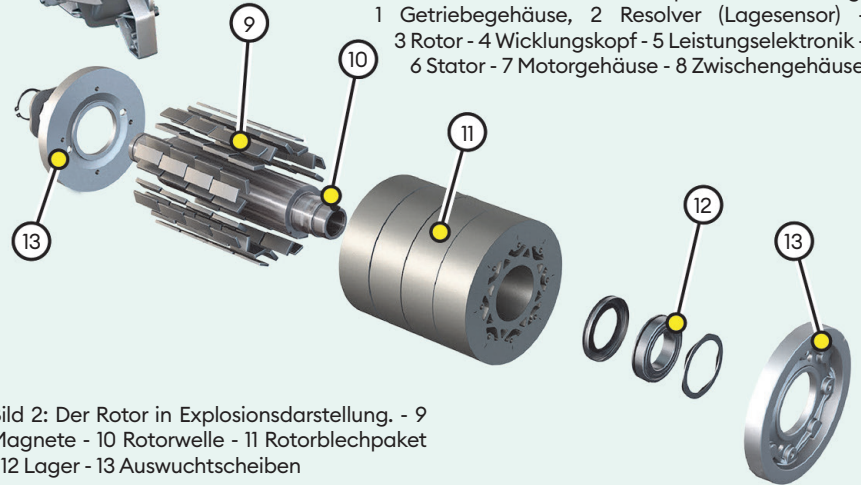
Der Rotor in Explosionsdarstellung. - 9 Magnete - 10 Rotorwelle - 11 Rotorblechpaket - 12 Lager - 13 Auswuchtscheiben
